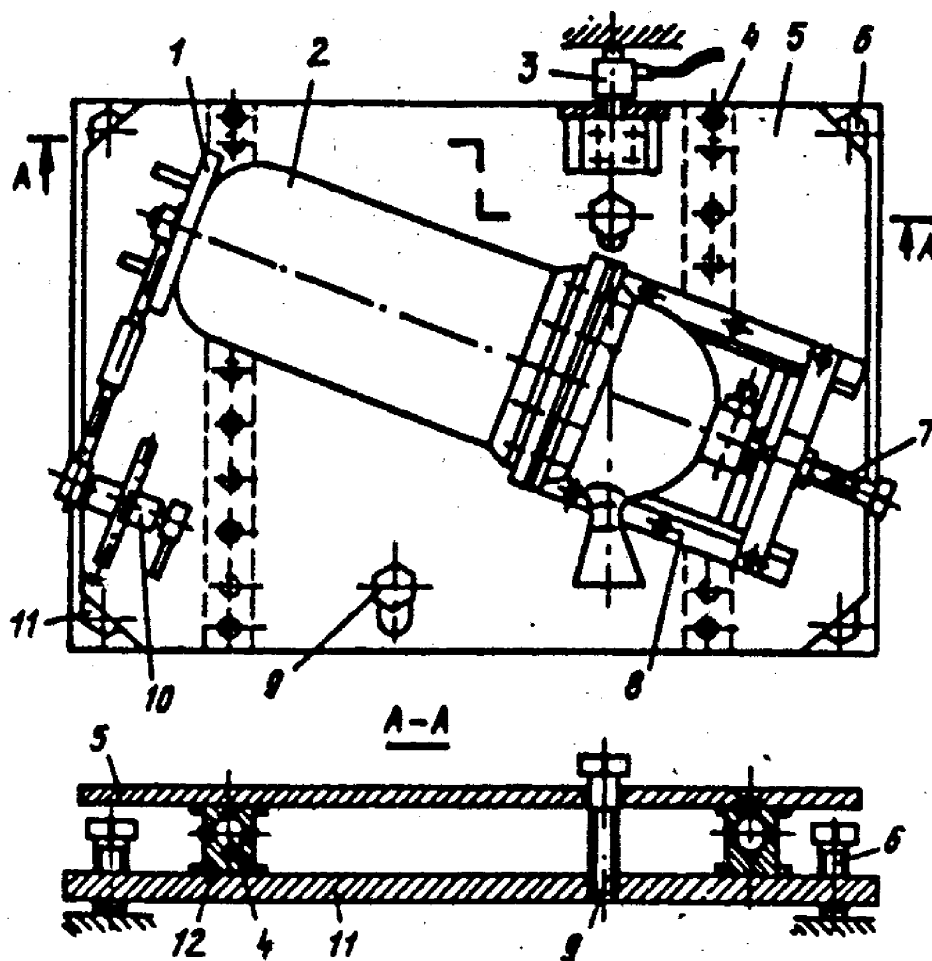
Установка на шаровых опорах для испытания ДСН малой тяги:
